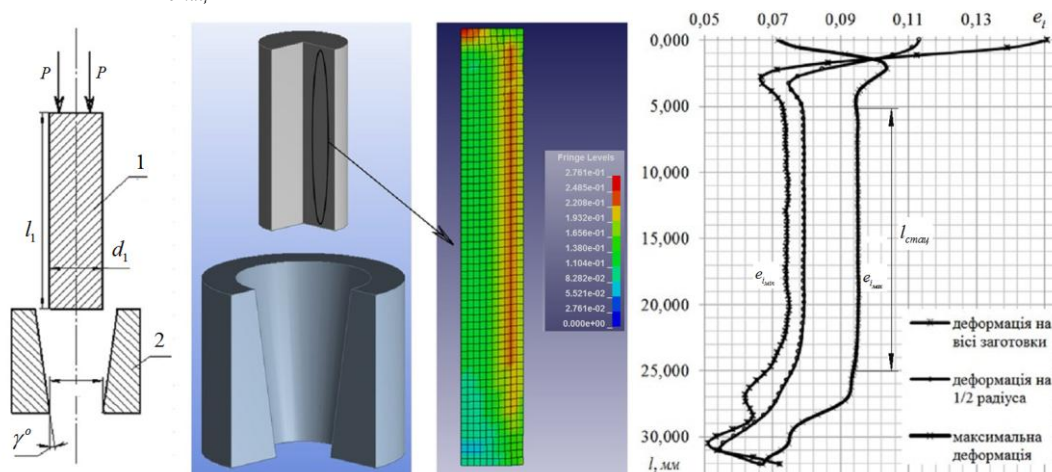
Редукування заготовки (1 – заготовка, 2-матриця)
